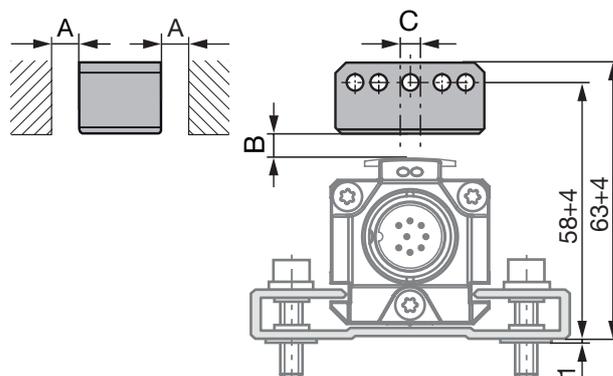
Dimensions et distances avec le capteur de position BTL6-A-3801-2
